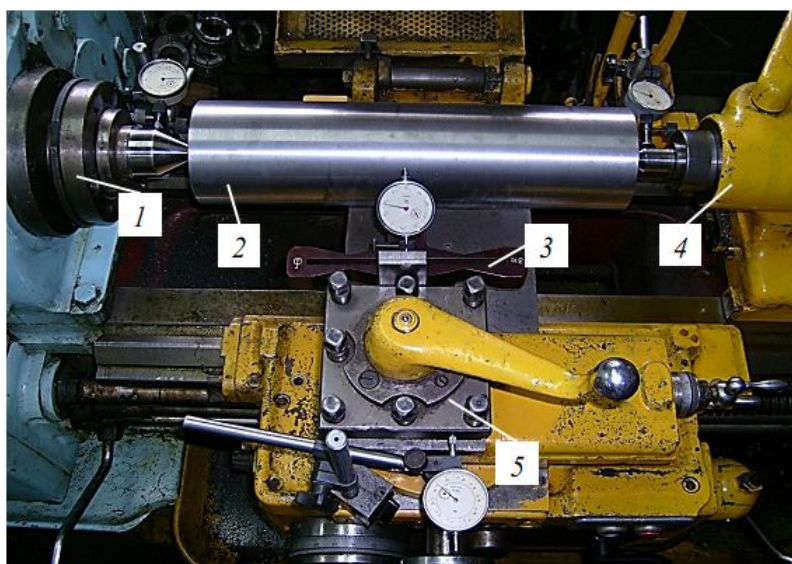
Установка для измерения податливости токарного станка при обработке заготовки в центрах: 1 – передняя бабка; 2 – заготовка; 3 – динамометр ДОС-3тс; 4 – задняя бабка; 5 – резцедержатель
